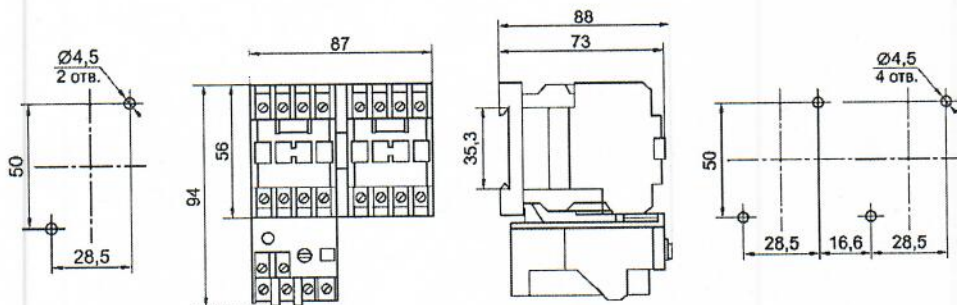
Пускатель реверсивный ПМ12-010 10А.
